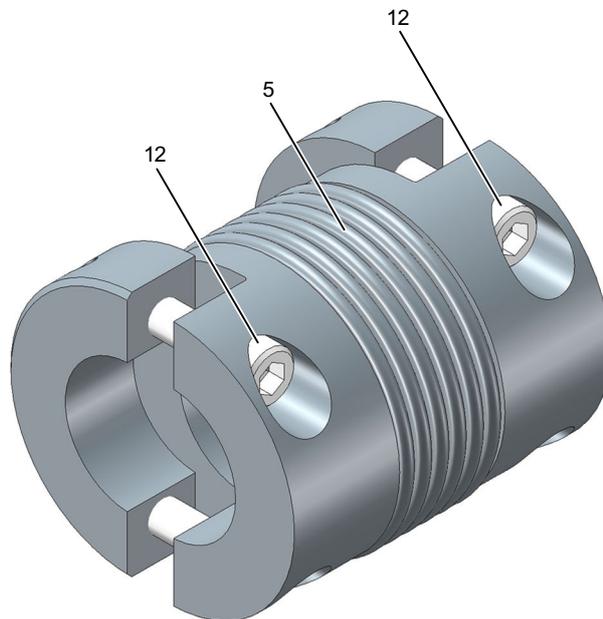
Ersatzteilzeichnung für Bauart SHH
